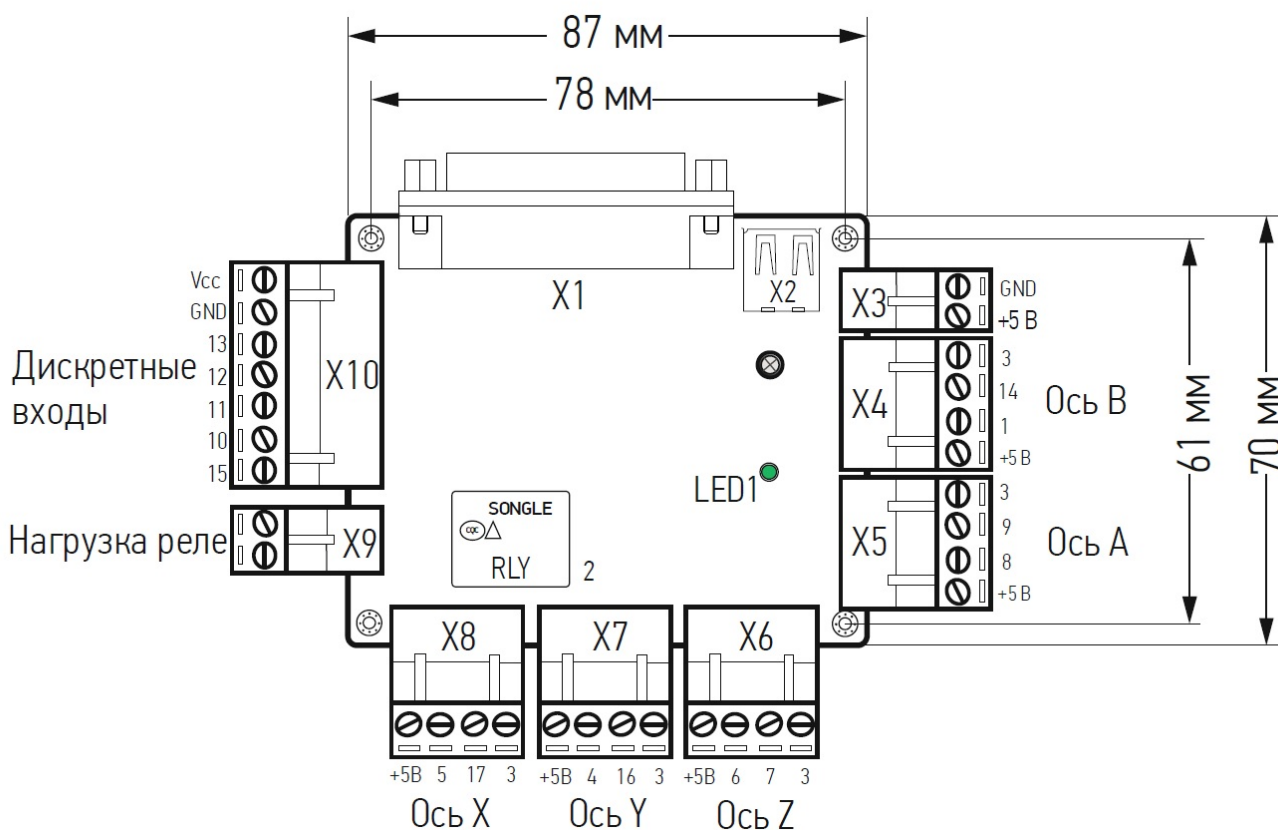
Габаритные размеры и распиновка платы DXB-55
